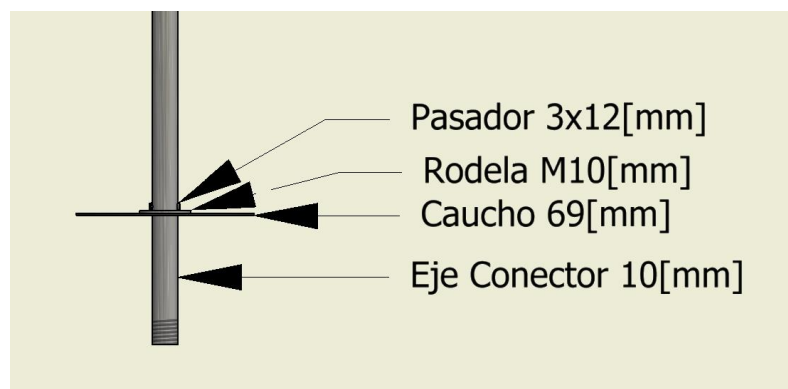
DIMENSIONES DE LA BOMBA
